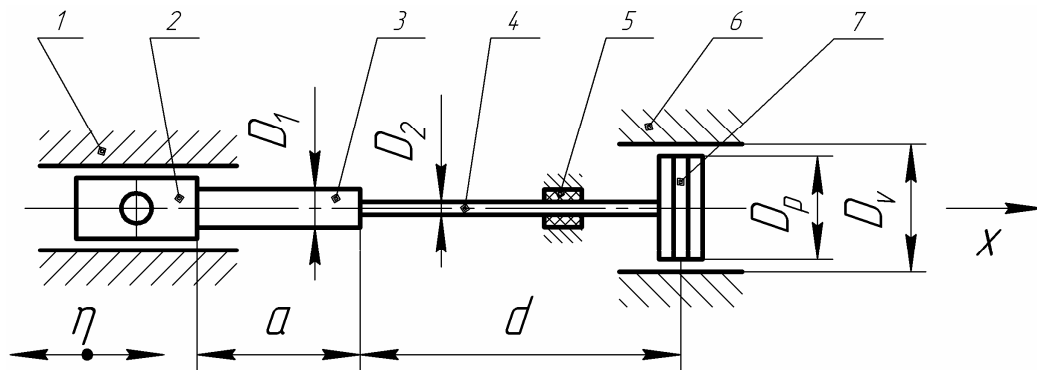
Схема встановлення штока в насосі: 1 – напрямні станини; 2 – крейцкопф; 3 – надставка штока; 4 – шток; 5 – ущільнення штока; 6 – циліндрова втулка; 7 – поршень
